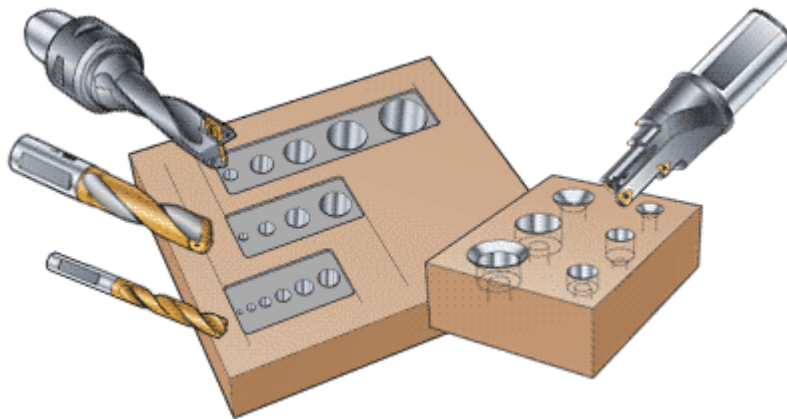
Exemplo do Processo de Usinagem – Furar [70].
